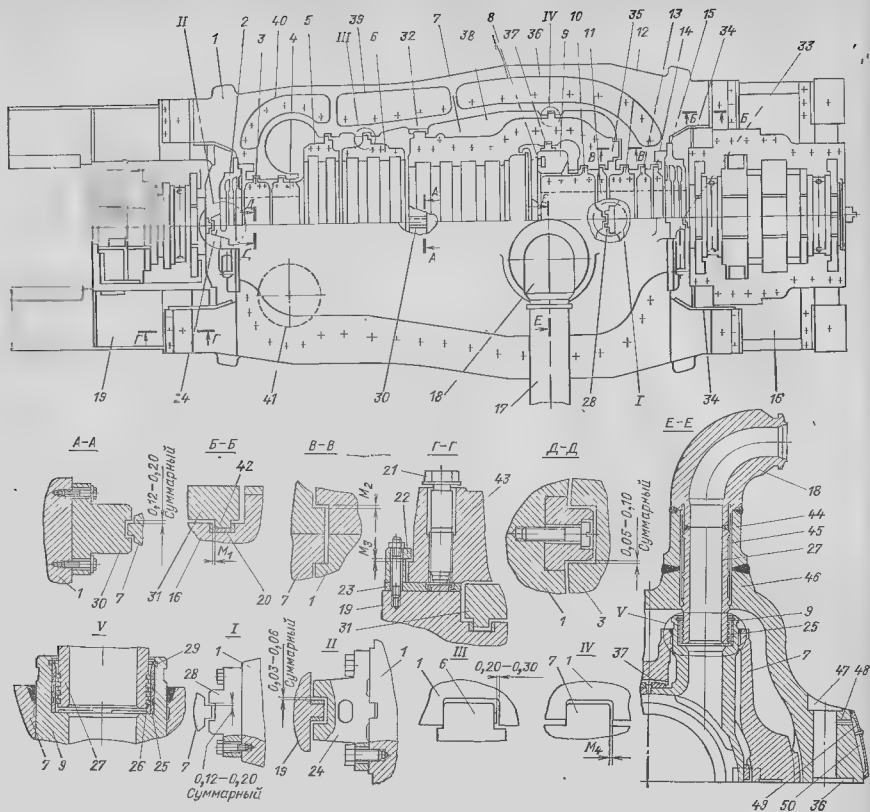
Цилиндр высокого давления турбины К-500-240-2 (вид сверху)
